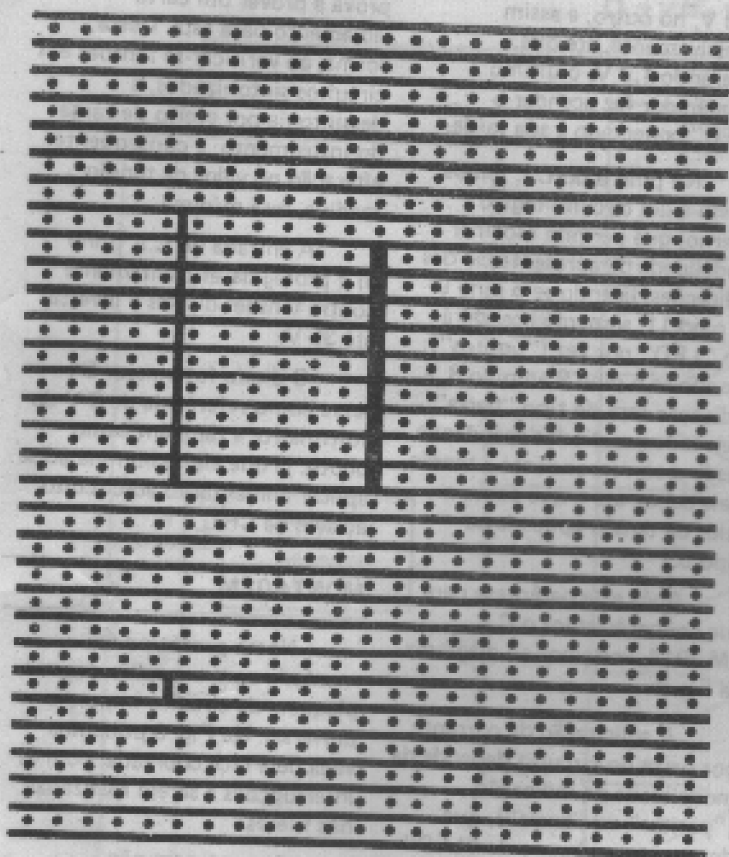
Plaqueta de circuito impresso universal utilizada na montagem do "LED Voltmeter", vista pela face cobreada, com os pontos onde os filetes de cobre devem ser interrompidos.
